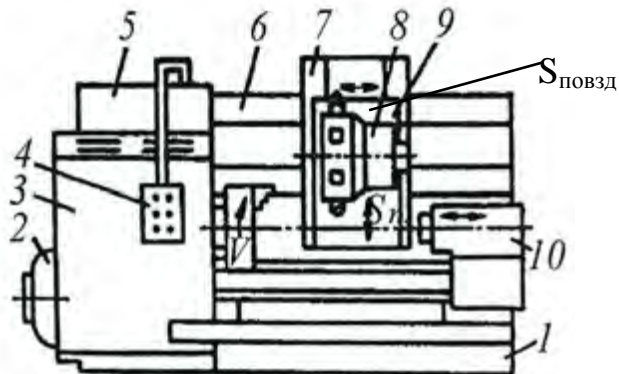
Загальний вид токарно-гвинторізного верстату з ЧПК
